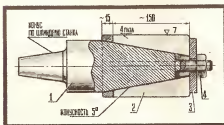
Притир для обработки цилиндра: 1 — оправка; 2 — чугунная разрезная втулка; 3 — шпатель; 4 — гайка.
